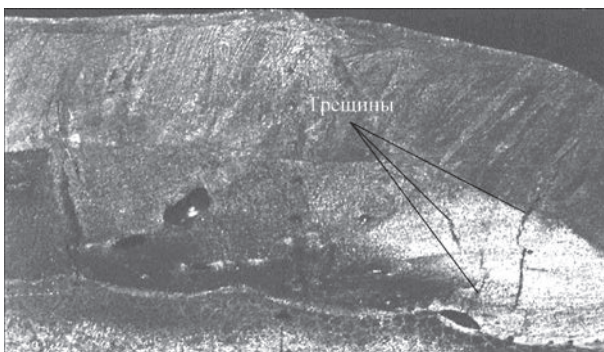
Продольные трещины в наплавленном слое (1011), выполненном дуговой наплавкой сплошной проволокой в активном газе (процесс 135, наплавленный металл группы Fe1 [4–6])
